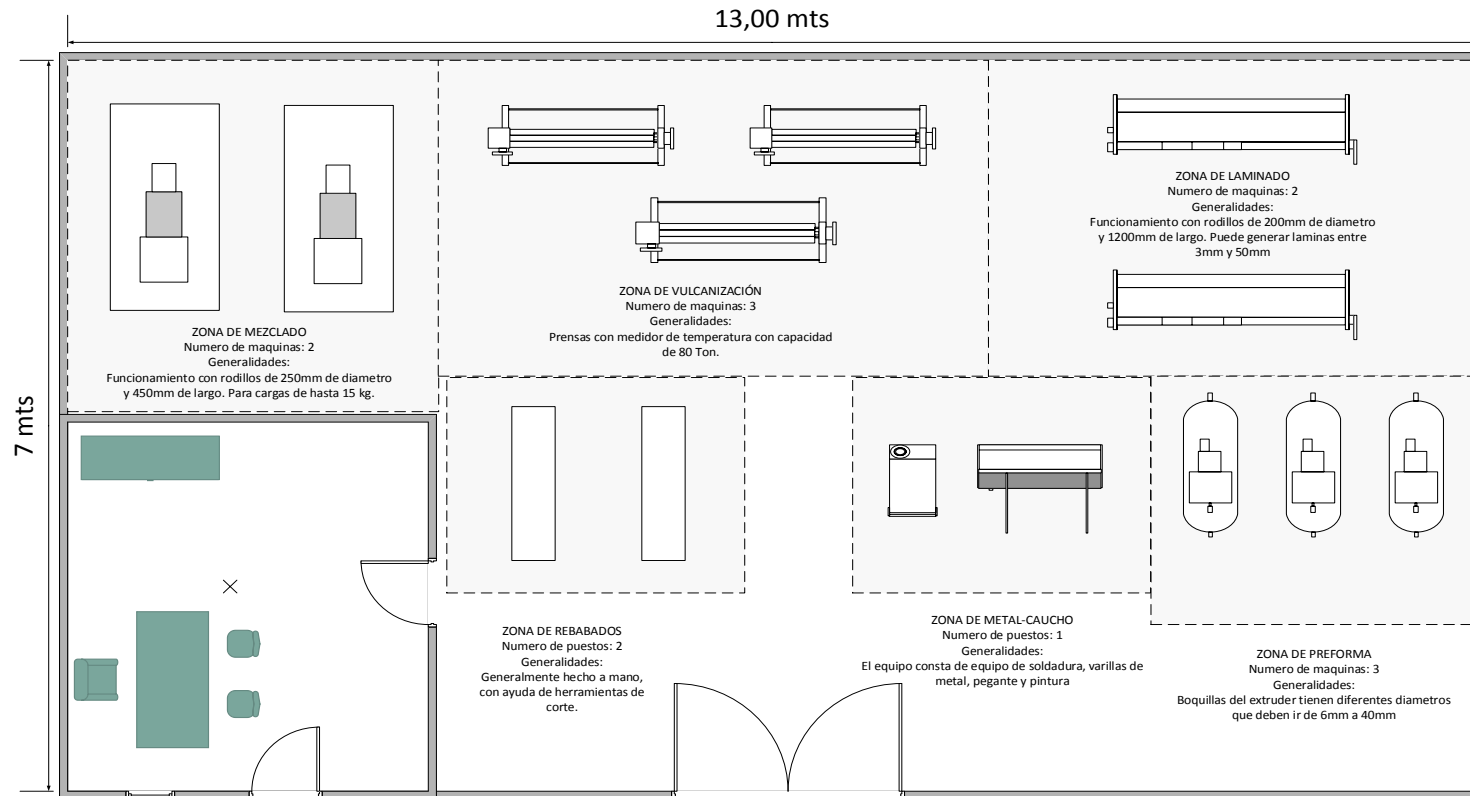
Disposición de la planta de la empresa Empaques de caucho Ortiz
